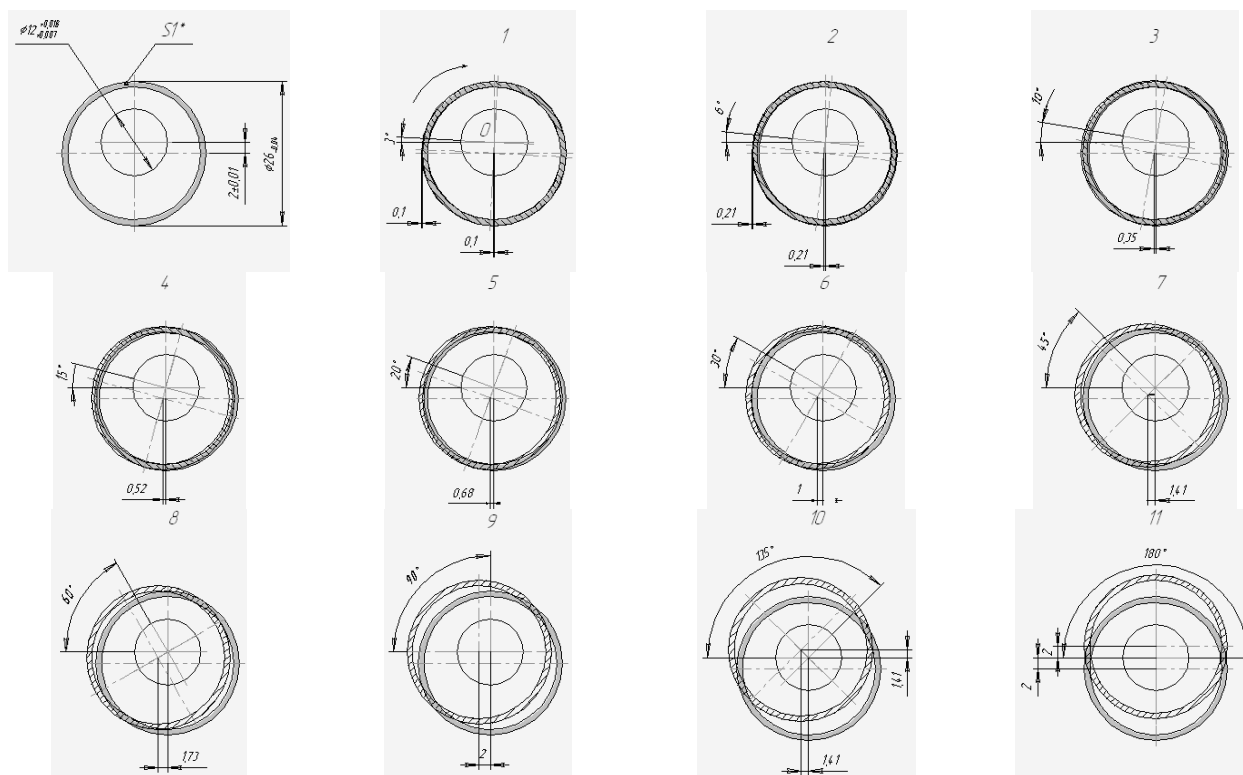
Последовательность процесса резки трубчатой заготовки одновременным сдвигом и кручением
